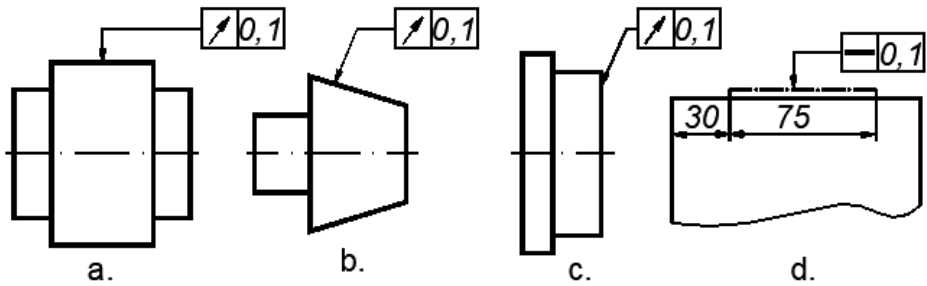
Reguli de înscriere pe desene a toleranțelor de formă și poziție.
